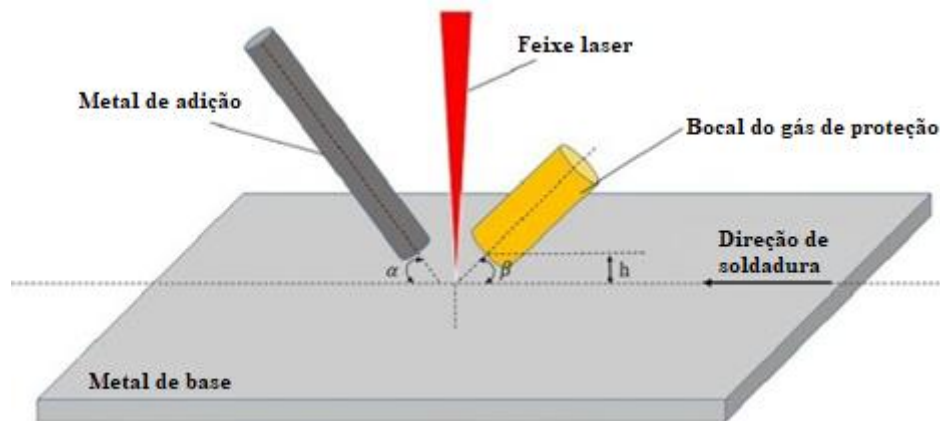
Esquema do processo de soldadura híbrida com material de adição e gás de proteção. (Adaptado de [9])
